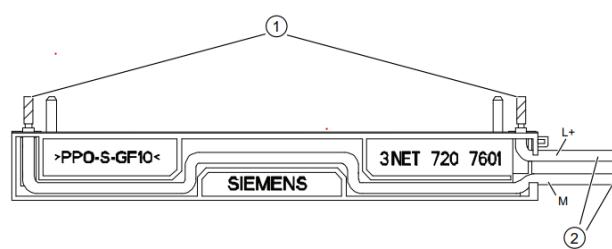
Укладка соединительных кабелей напряжения нагрузки в камеру кабеля. Наружный диаметр кабелей > 2 мм (вид снизу)
